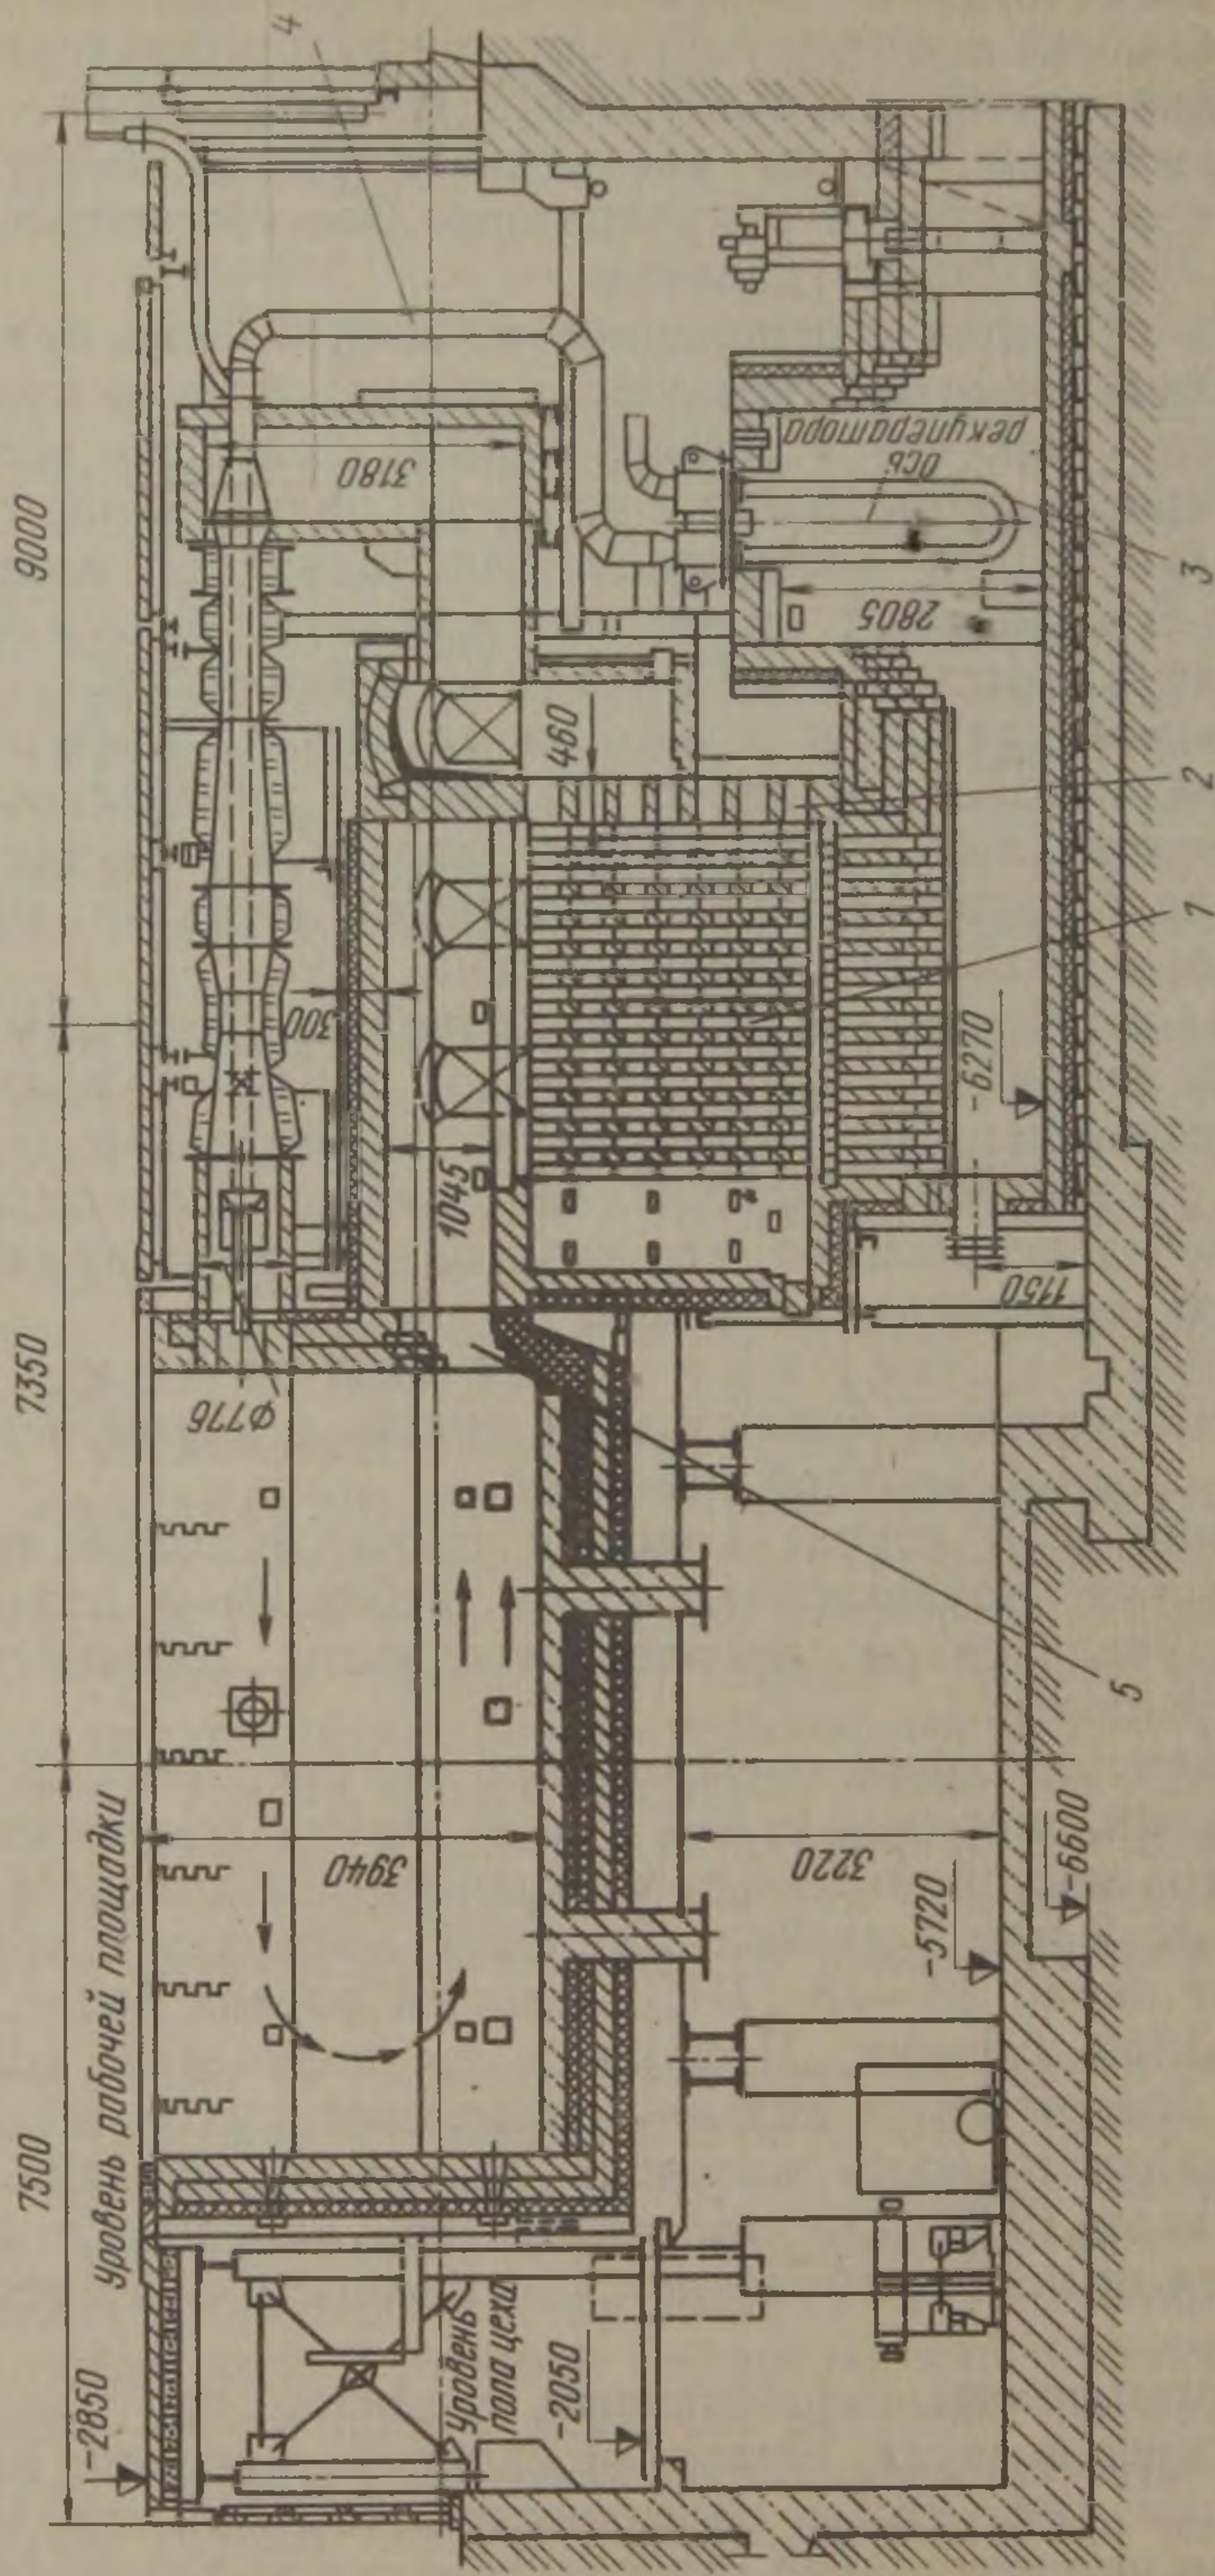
Нагревательный колодец с одной верхней горелкой:
